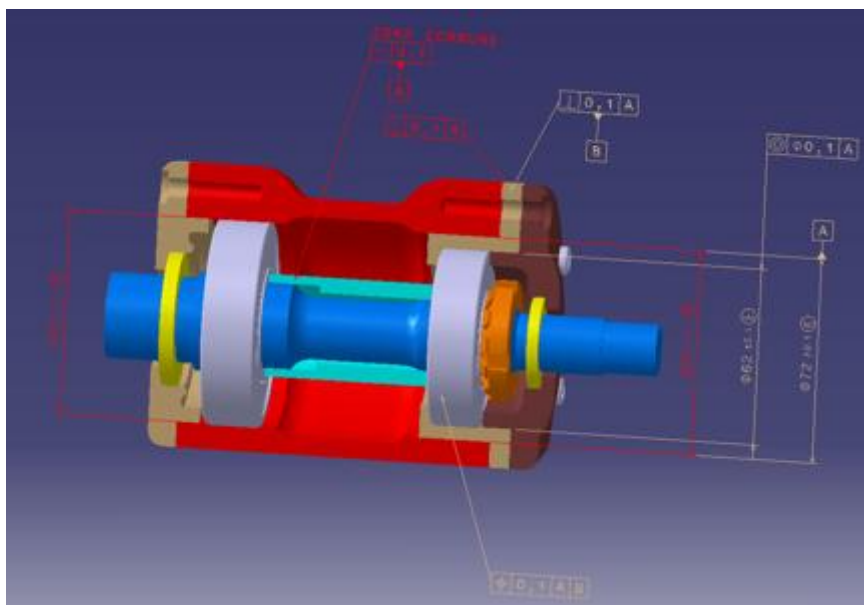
Un exemple d'analyse du tolérancement sur des pièces rigides (ici, un montage de roulements).
